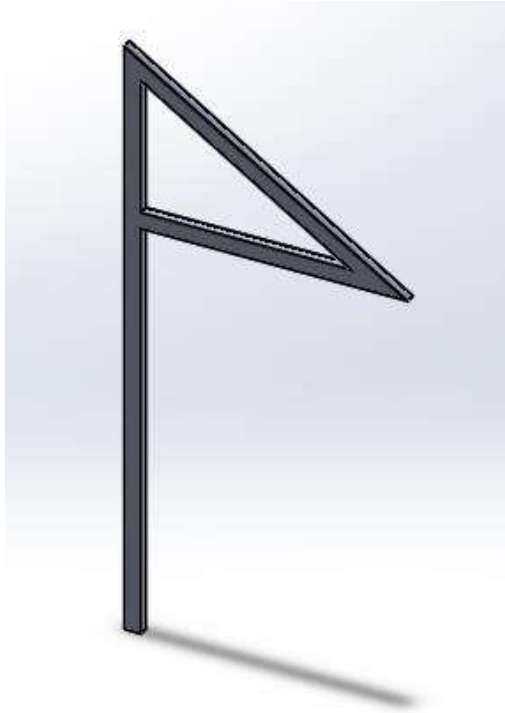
Subconjunto de estructura inferior. Pilar
